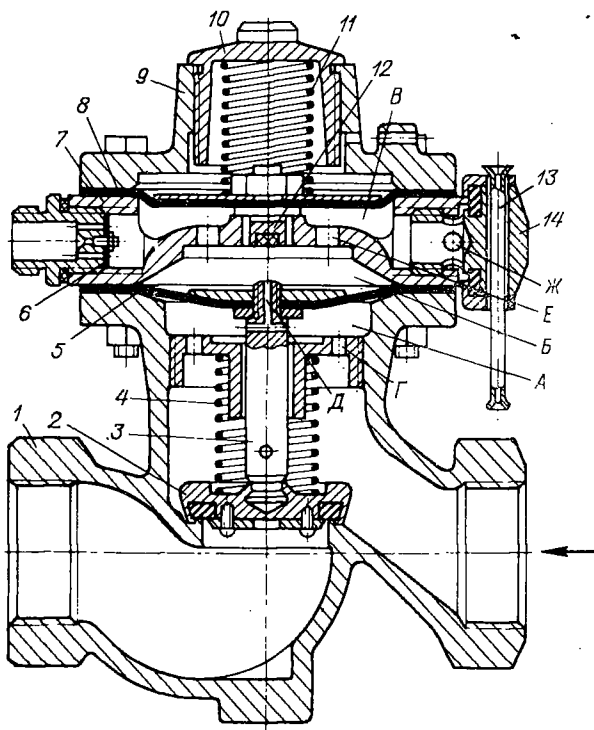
Предохранительный клапан-отсекатель ПКК-40М.
